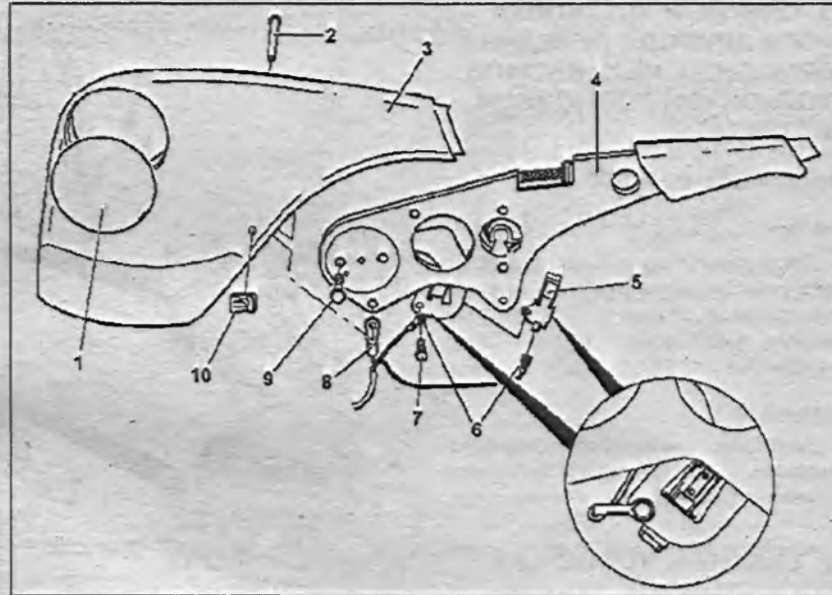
Рычаг привода стояночной тормозной системы: 1, 3 - Крышки; 2 - Блокировочный палец; 4 - Рычаг привода стояночной тормозной системы; 5 - Датчик положения рычага привода стояночной тормозной системы; 6 - Разъемы проводки; 7, 9 - Болты; 8 - Трос привода стояночной тормозной системы; 10 - Зажим.
